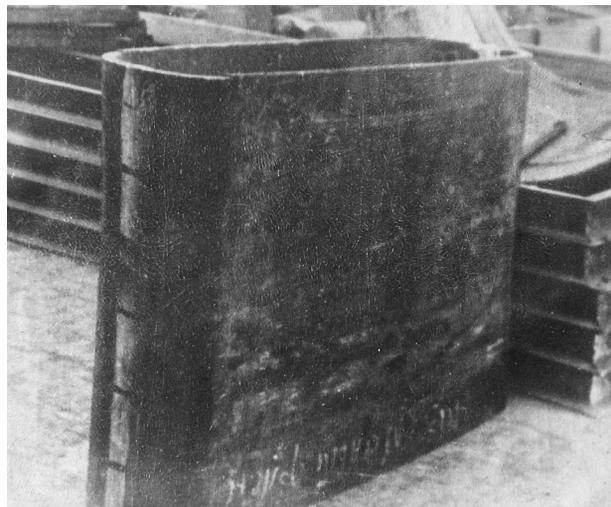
Сварная медная изложница кристаллизатора для вакуумно-дуговых и электрошлаковых печей
